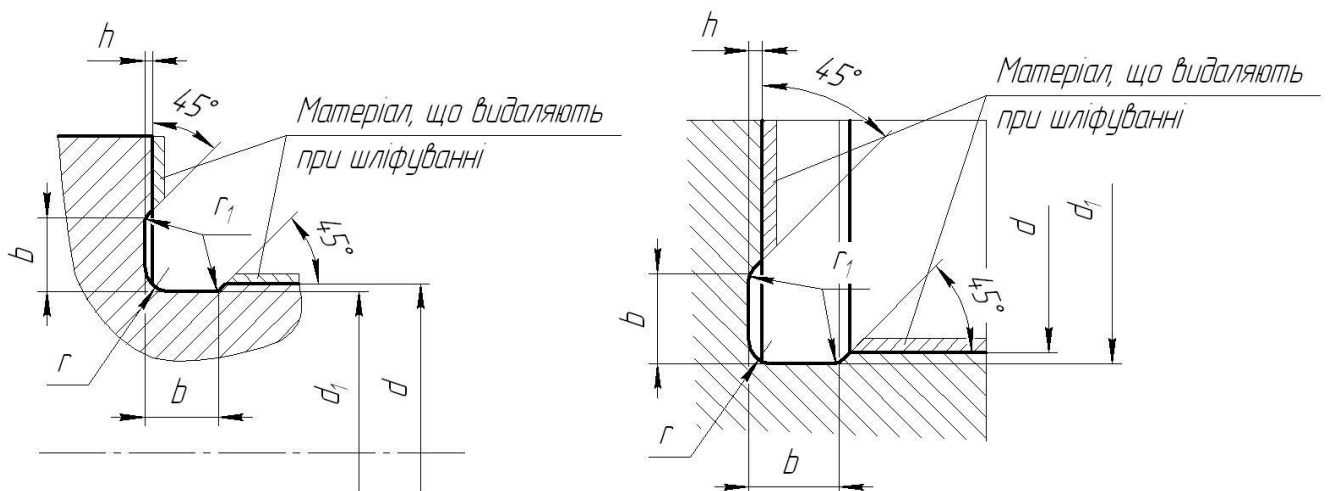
Канавки при внутрішньому й зовнішньому шліфуванні по циліндру й торцю одночасно
